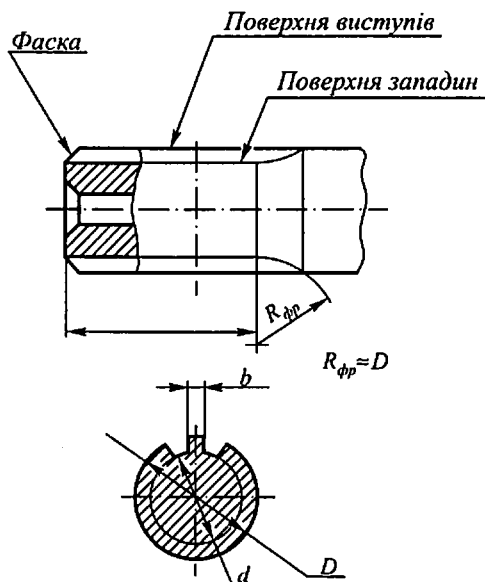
Шліцевий вал із зубцями прямобічного профілю
